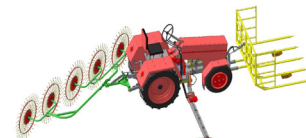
3D-модель комбинированного агрегата для заготовки кормов
